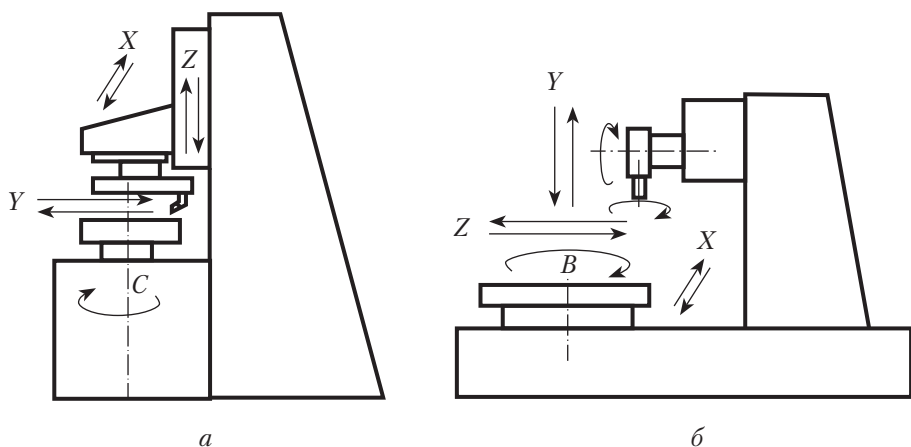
Токарный вертикальный (а) и горизонтально-расточной (б) станки с ЧПУ
